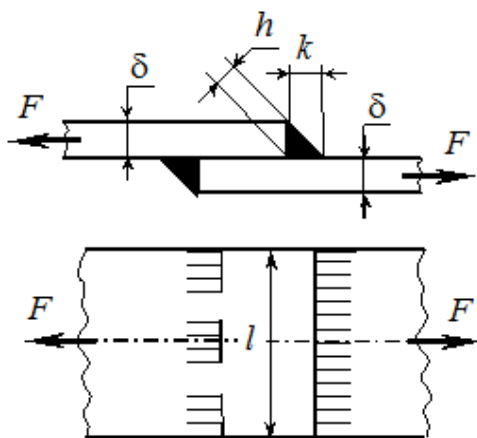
Розрахункова схема зварного напусткового з'єднання на міцність
